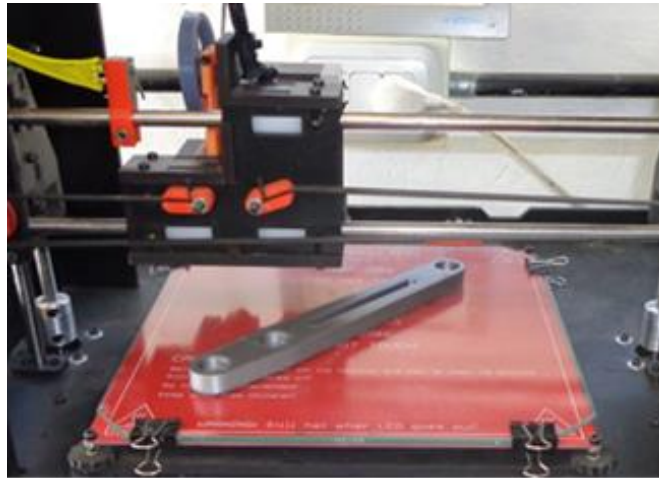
Impresión de biela principal mediante la tecnología (FDM) Fused Deposition Modeling
